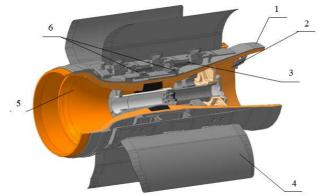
Конструктивно-компоновочная схема проворачивающегося блока стабилизаторов
